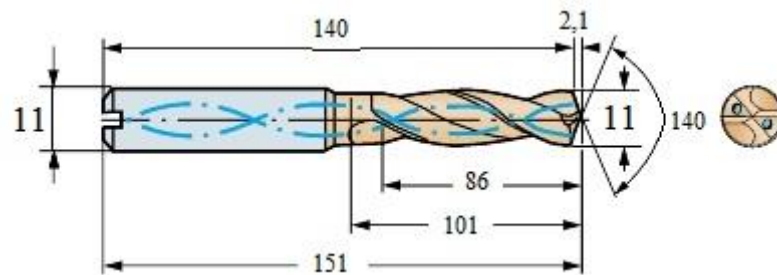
Сверло Ø11 CoroDrill Delta-C R840–1100–70–A1A 1220
